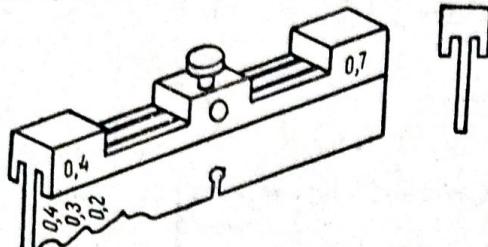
Фуганок для лучковых пил конструкции Н. А. Возного
